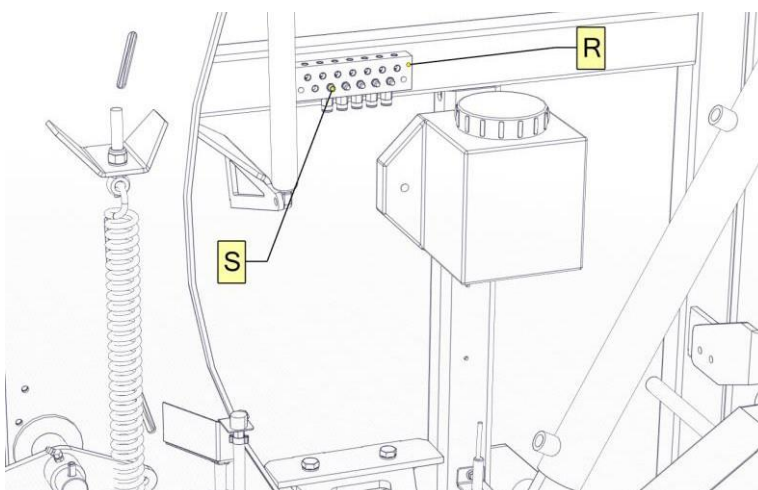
Центральная система смазки подшипников на левой стороне пресс-подборщика
